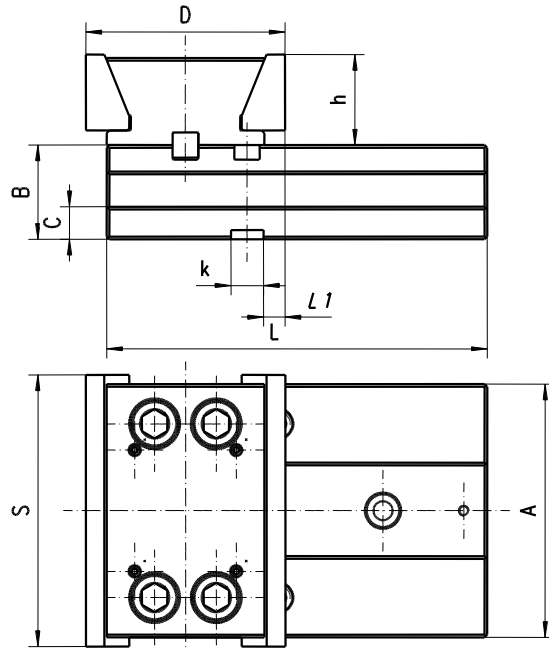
Hauptmaße des Schraubstocks, Typ 6624.
